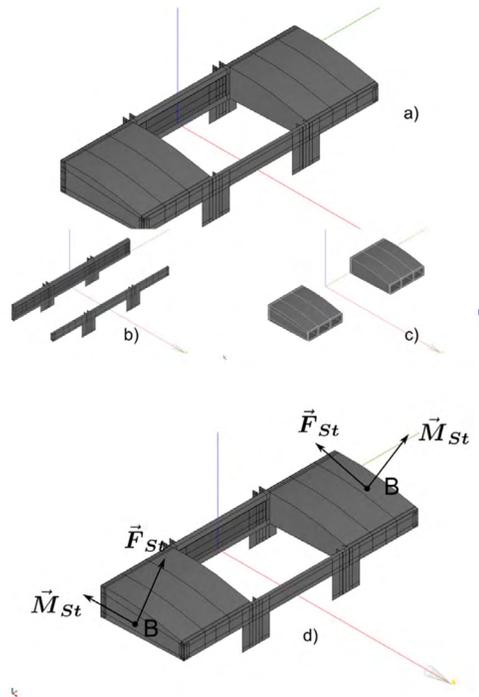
Cargas de la sección central: a) vista general; b) vigas; c) caja de torsión y; d) fuerzas sobre la estructura
